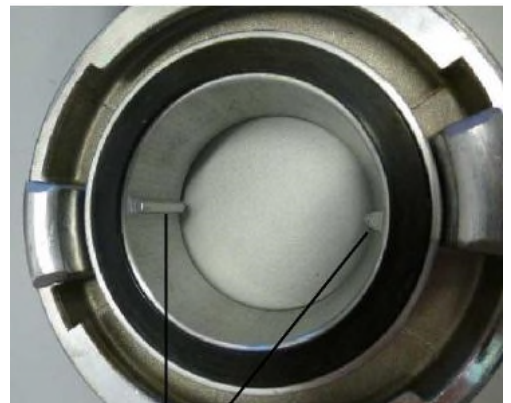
(©KUVB) / Innenliegender Gewindestutzen mit Stegen für Spezialwerkzeug
